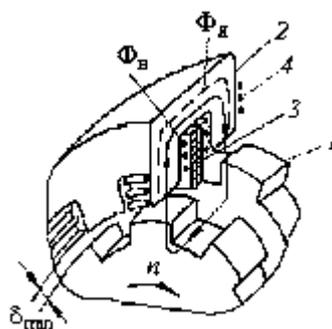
Конструктивная схема индукторного двухпакетного генератора
